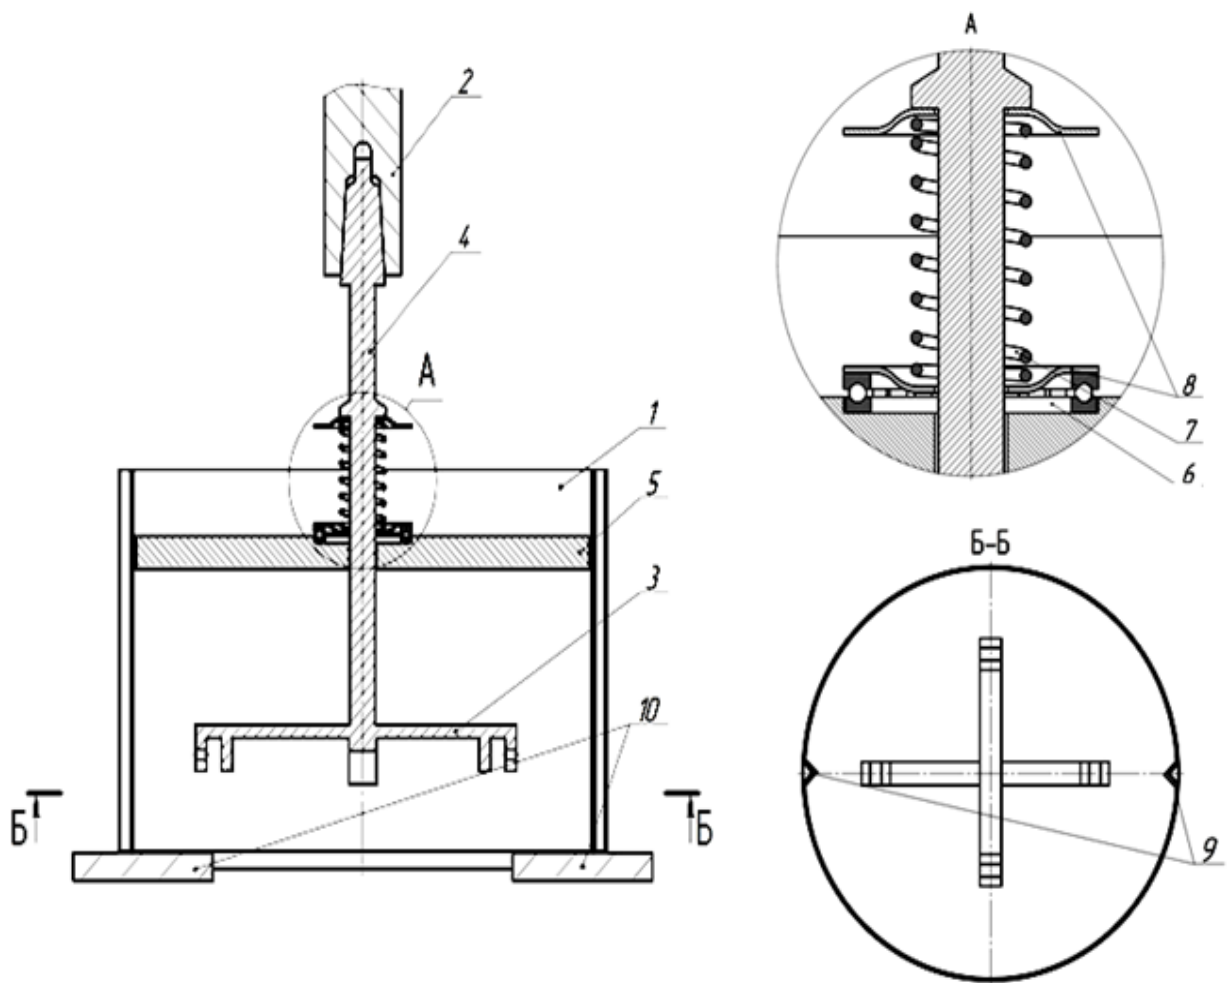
Общий вид установки для исследования износостойкости рабочих органов сельскохозяйственных орудий на базе вертикально-сверлильного станка
